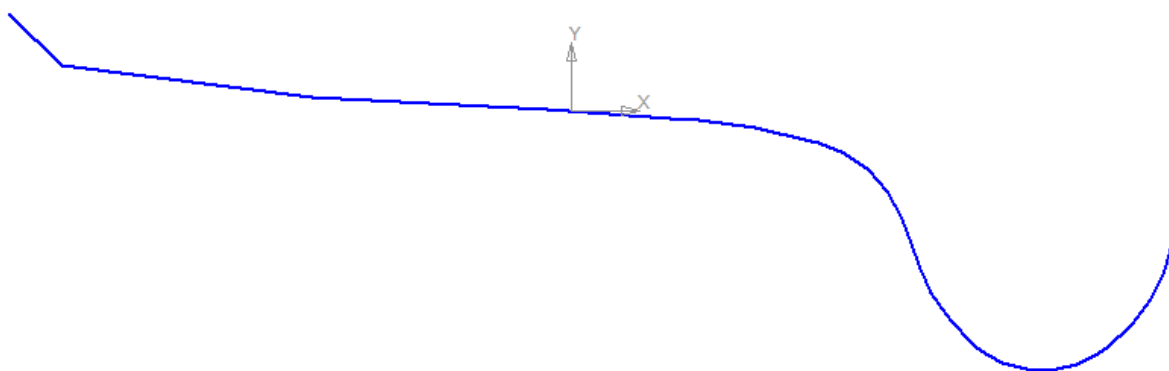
Профиль колеса в САПР КОМПАС 3D
